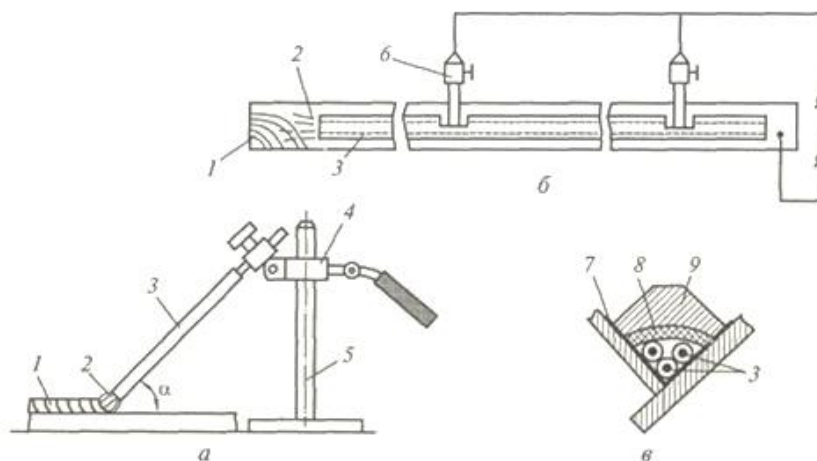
Схема сварки наклонным (а) и лежачим (б, в) электродами:
